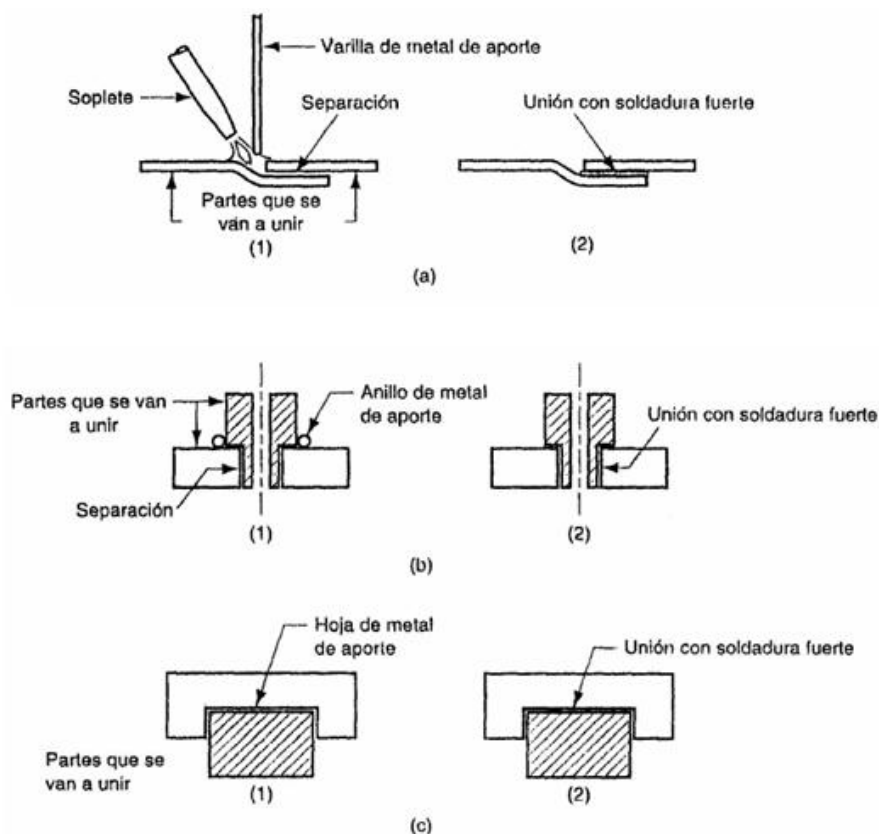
Varias técnicas para aplicar metal de aporte en la soldadura fuerte: (a) soplete y varilla de aporte, (b) anillo de metal de aporte a la entrada de la separación y (c) hoja de metal de aporte entre superficies de partes planas. Secuencia:(1) antes y (2) después. [5]
